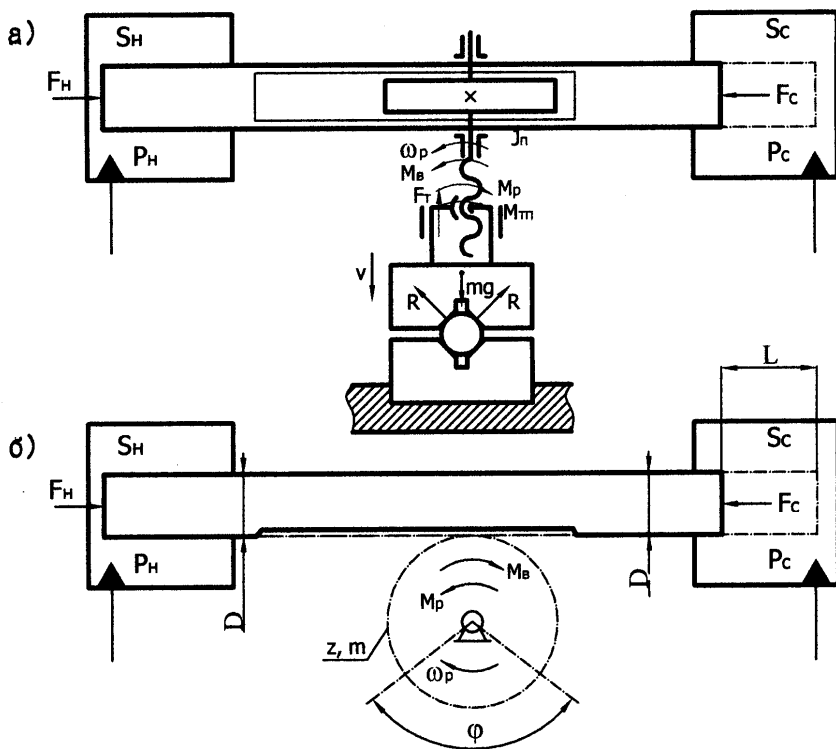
Расчетные схемы вращающего развиваемого и расчетного момента (а) и параметров (б) поворотного гидродвигателя в виде силового цилиндра с реечной передачей привода зажимного механизма станочного приспособления
